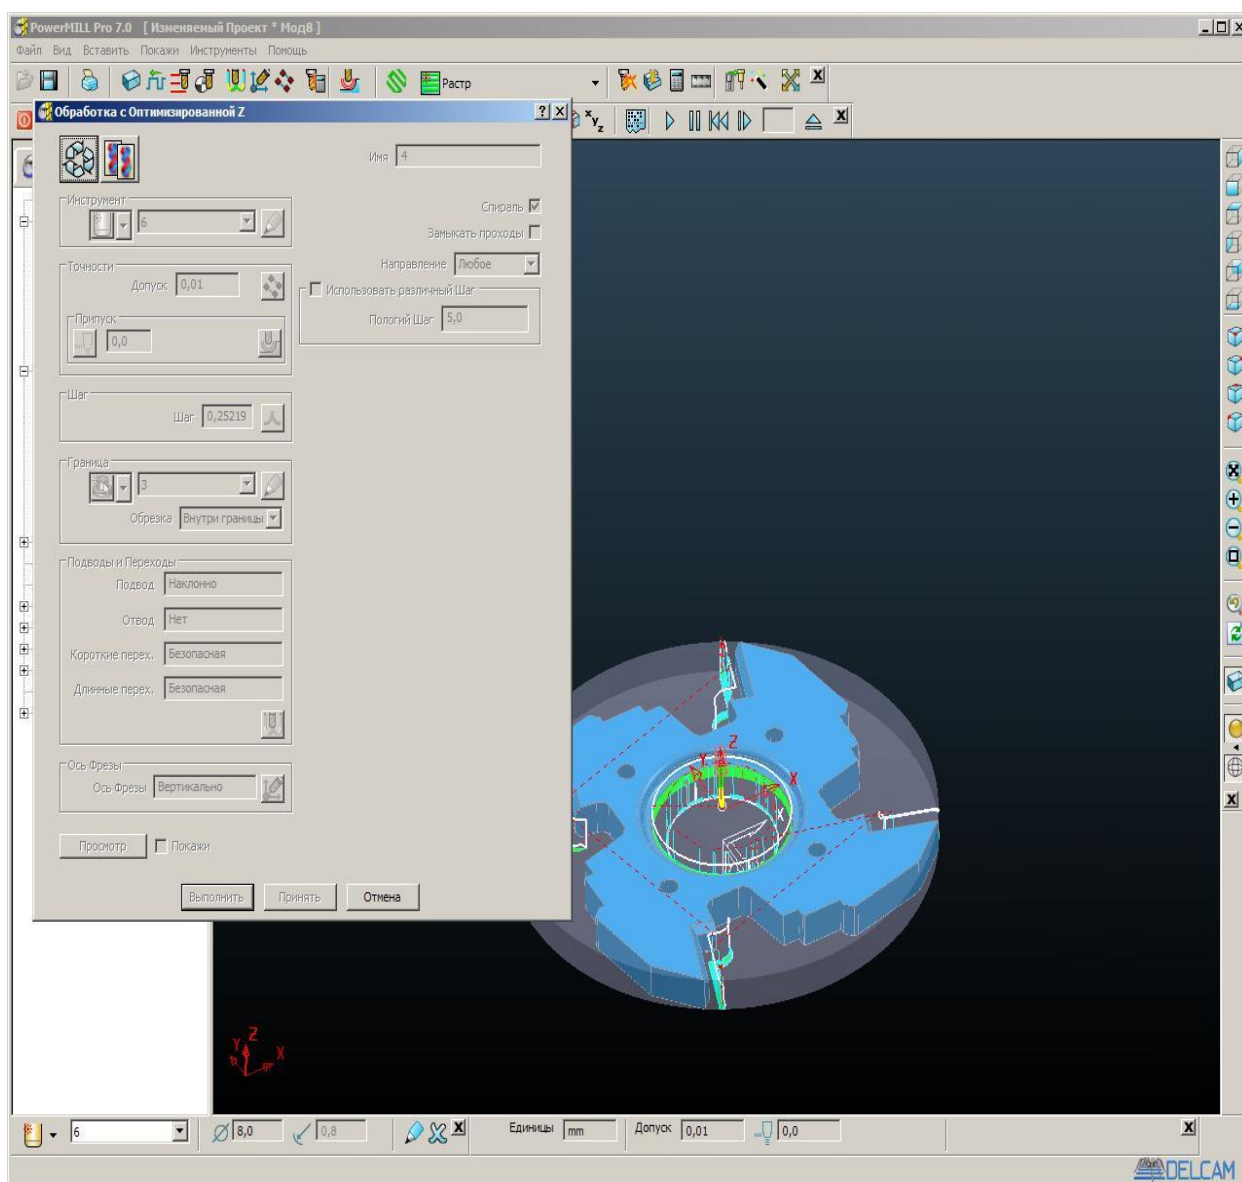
Заготовка деталі «диск RI000909 ротора RI9000909000d»
